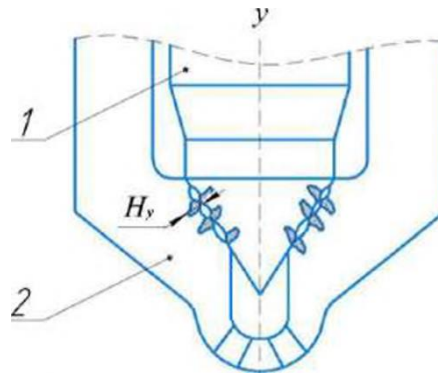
Епюра контактних напружень конусної поверхні сполучення "голка - корпус розпилювача форсунки": 1 – голка; 2 – сідло корпусу розпилювача;  $H_y$  – товщина поверхневого шару, що накопичує напруження удару [22].
